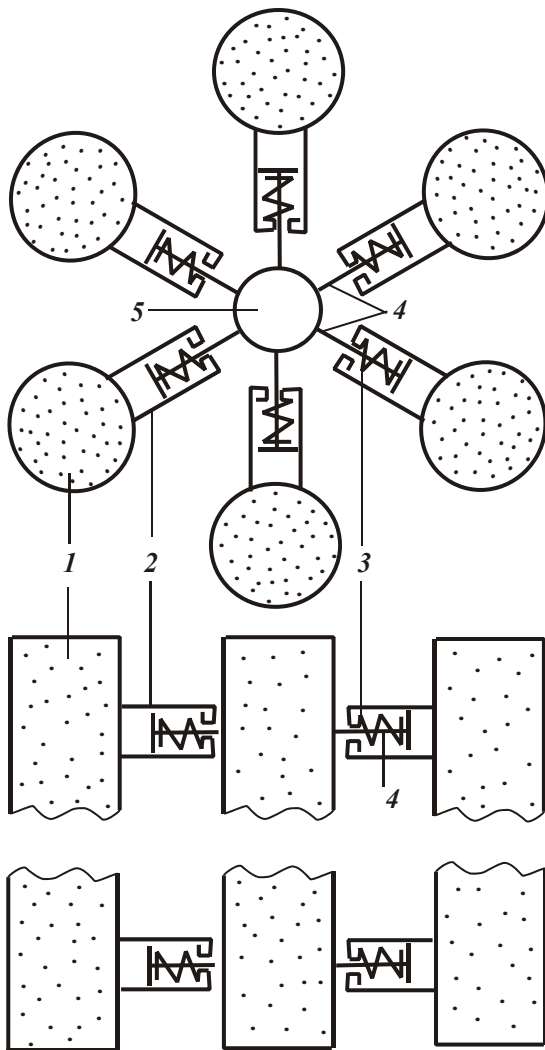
Инструмент для шлифования внутренних поверхностей: 1 – шлифовальный брусок; 2 – цилиндр; 3 – пружина; 4 – штырь (спица); 5 – вал.
